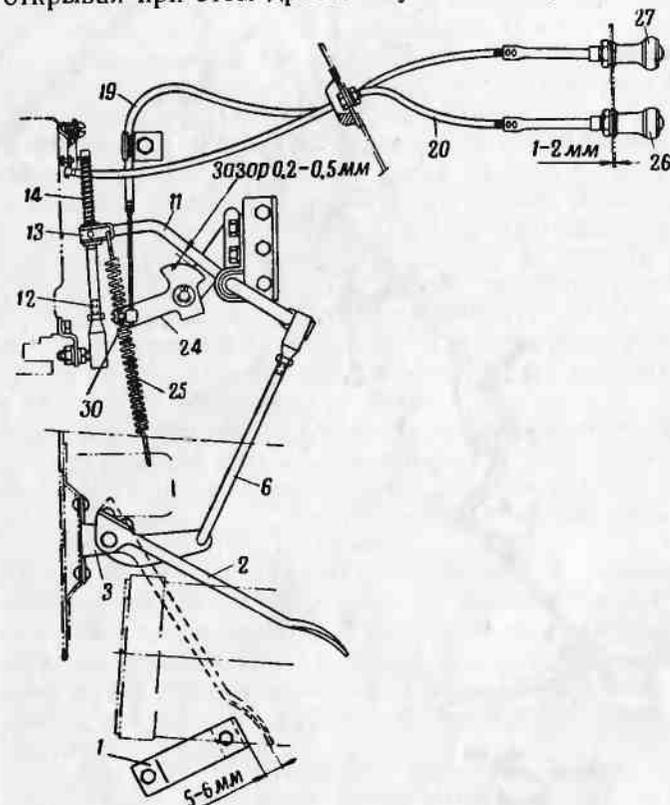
Детали привода управления заслонками карбюратора: 1 — ограничитель хода педали; 2 — педаль; 3 — кронштейн педали; 6 — сошка педали; 11 — валик педали; 12 — тяга; 13 — палец правого конца валика педали; 14 — пружина; 19 — трос ручного привода управления дроссельной заслонкой; 24 — рычаг с эксцентриком ручного привода дроссельной заслонки; 25 — пружина; 26 — кнопка управления воздушной заслонкой; 27 — кнопка управления дроссельной заслонкой; 30 — винт крепления троса
